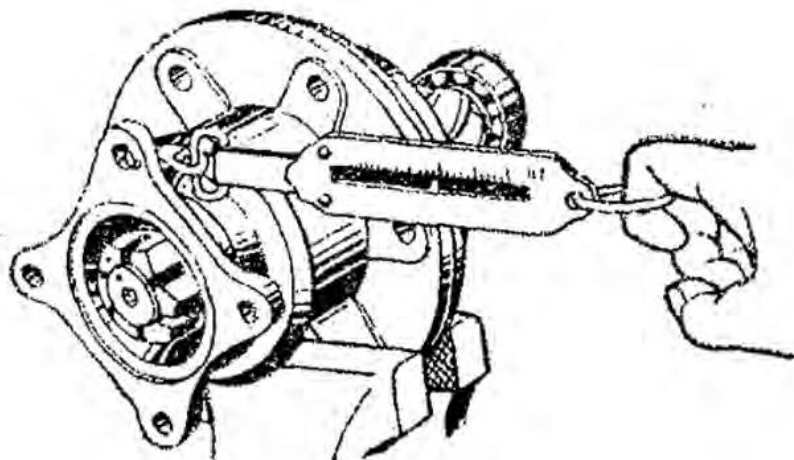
Проверка затяжки подшипников ведущей шестерни.
